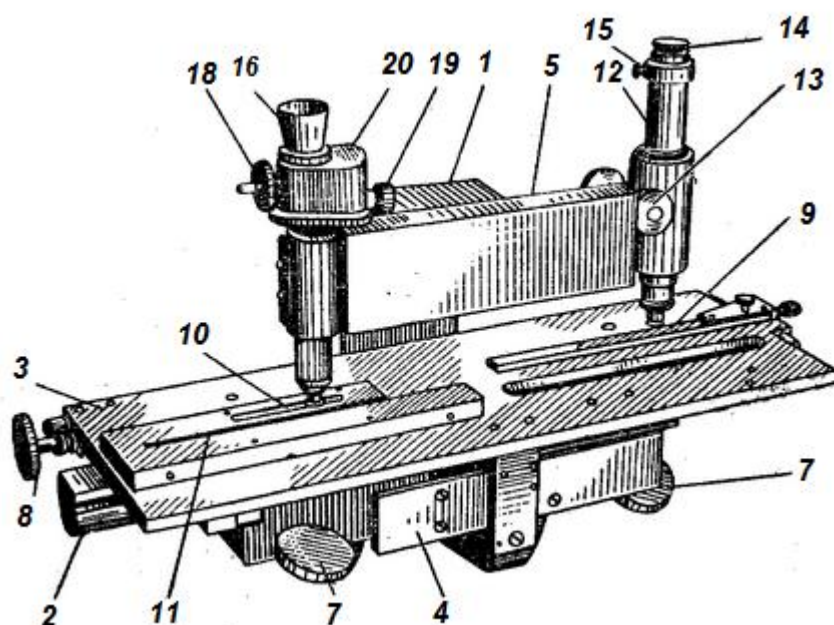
Горизонтальный компаратор, вид общий
